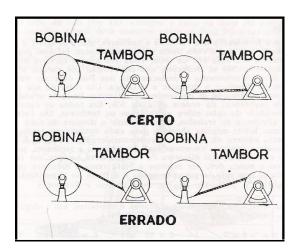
Passagem de cabo de aço de uma bobina para um tambor
